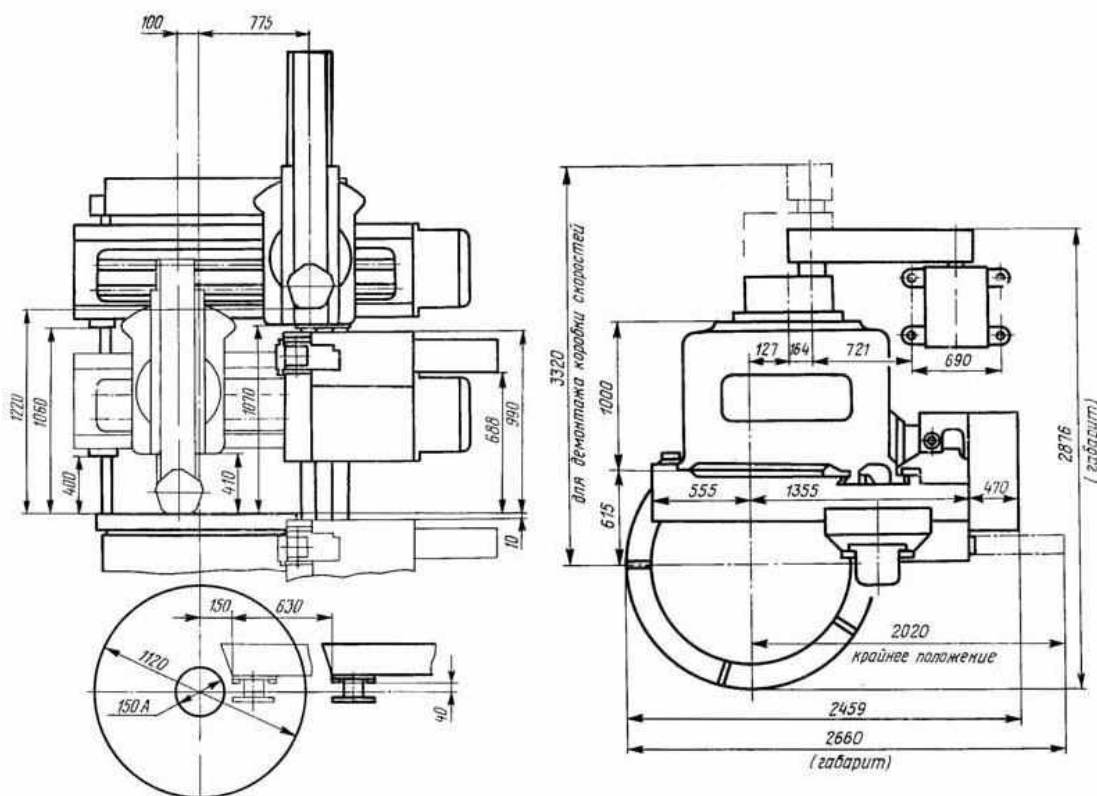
Схема робочої зони токарно-карусельного верстата 1510
